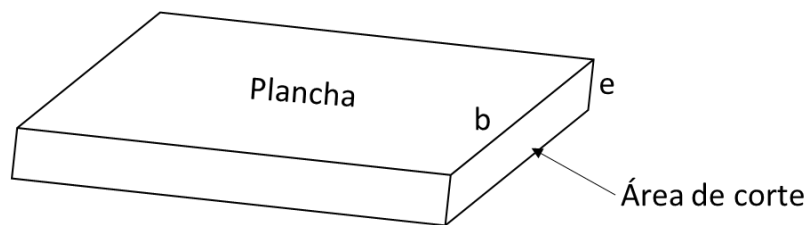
Espesor de la plancha de la tolva. Fuente: Elaboración propia.
